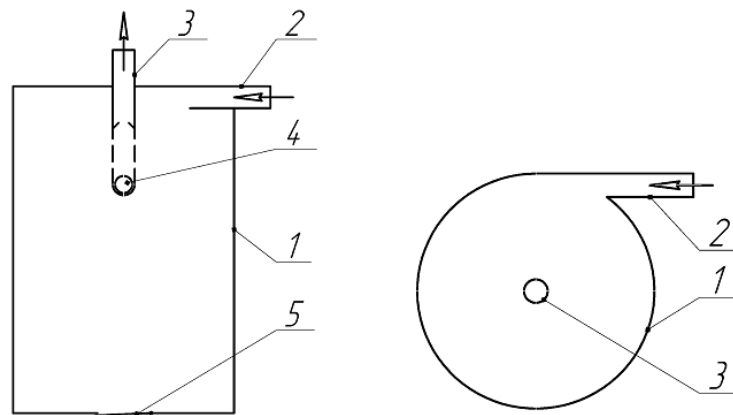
Схема вакуумного балона із приєднаними патрубками та поперечний переріз: 1 – корпус; 2 – впускний патрубок; 3 – випускний патрубок; 4 – кульковий клапан; 5 – зливна кришка
